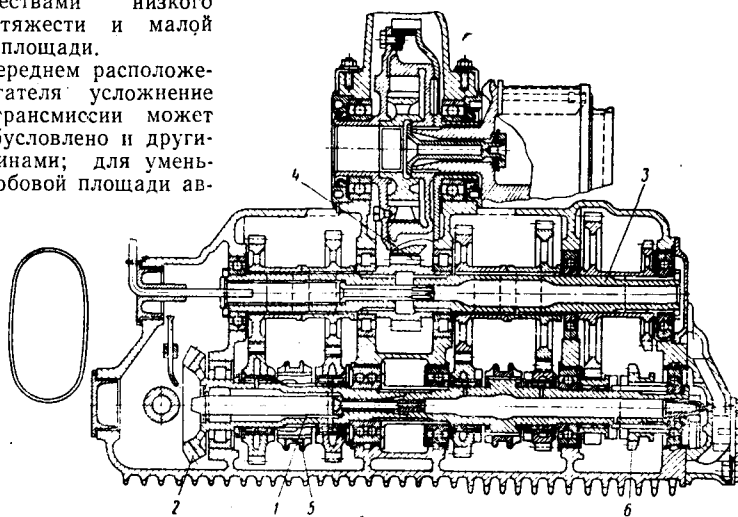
Пятиступенчатая коробка передач Мерседес Бенц для гоночного автомобиля с передним расположением двигателя.
